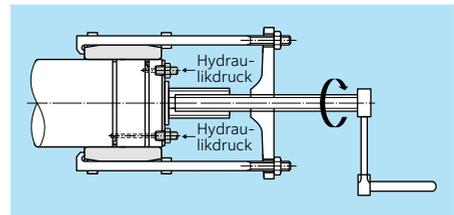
Demontage des Innenringes mittels Hydraulik
